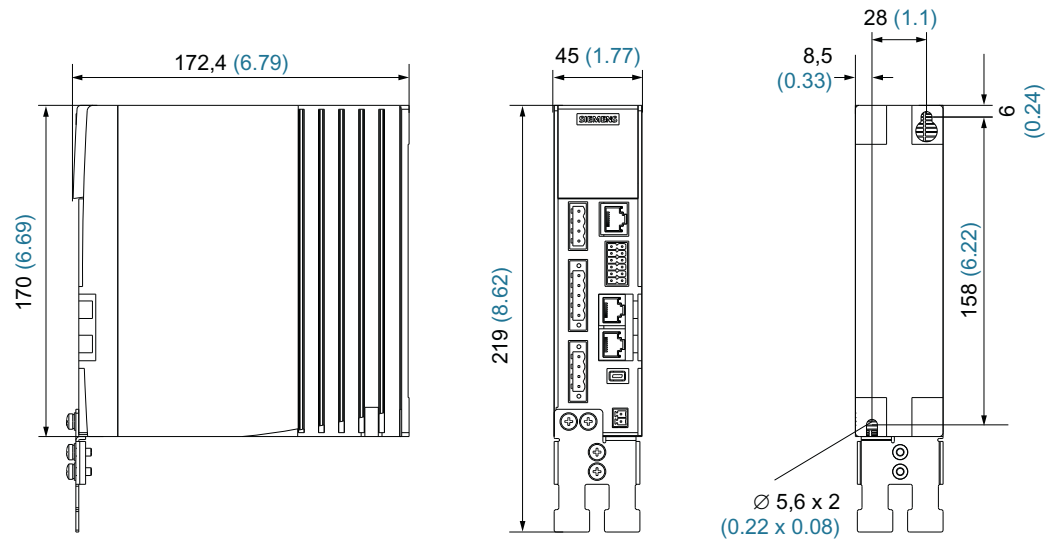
Maßzeichnung SINAMICS S210 FSA, Maße in mm (Inch)
